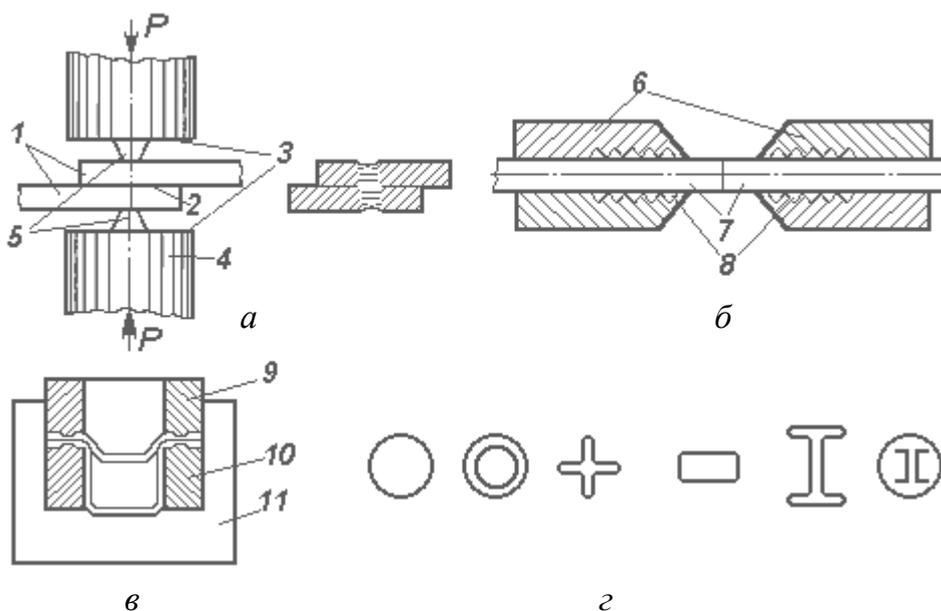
Принципиальная схема холодной сварки
